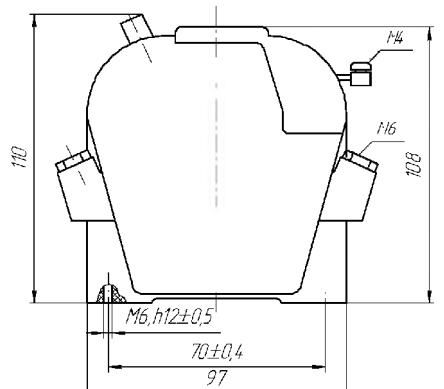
Габаритные, установочные и присоединительные размеры реле типа ТРТП-110, ТРТП-120, ТРТП-130.
